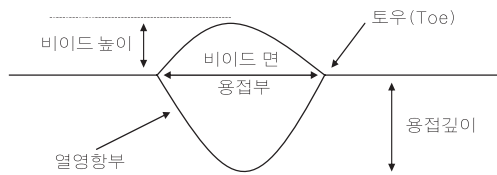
용접(Fusion weld)부 비이드(Bead)
